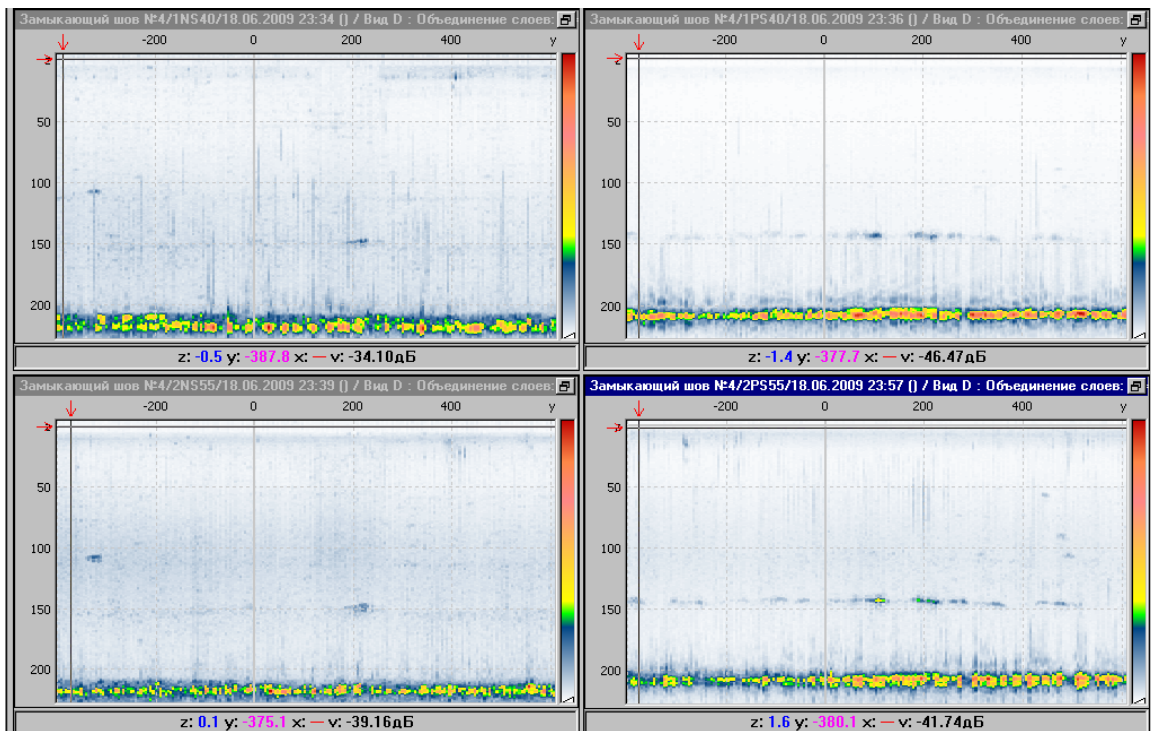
Участок сварного соединения с несплошностями.
